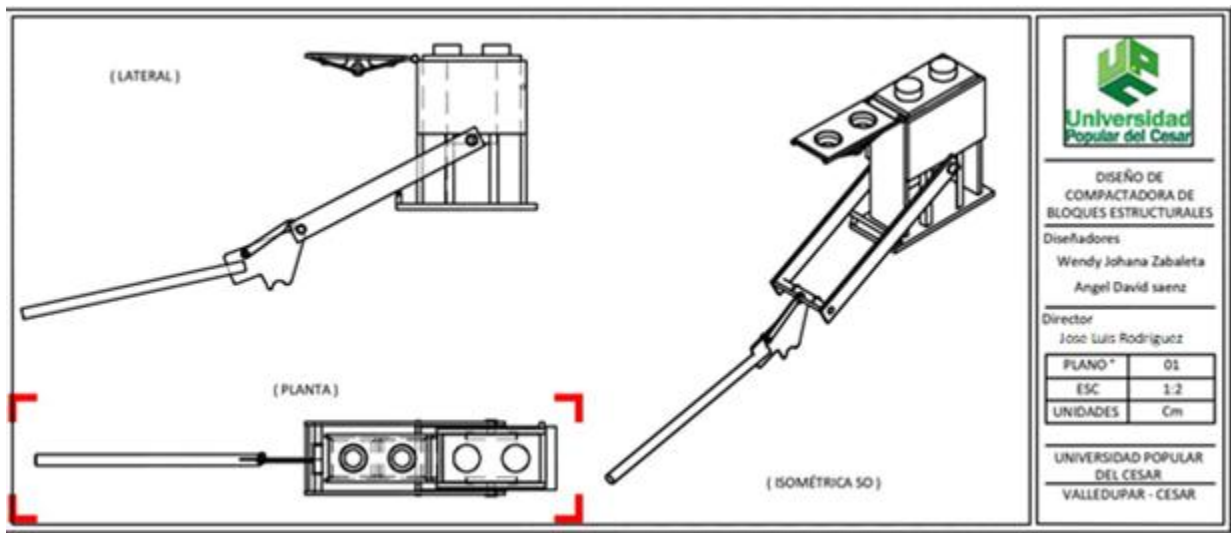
Plano de la vista lateral, en planta e isométrica de la máquina compactadora.
